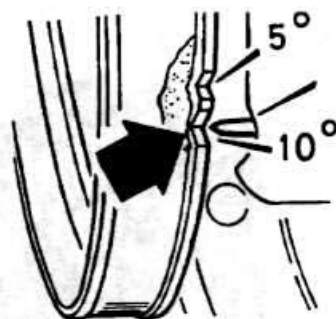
Риска 10° до ВМТ на шкиве коленвала совпадает со стрелкой на задней крышке ремня — для карбюраторных двигателей 1,4 л
